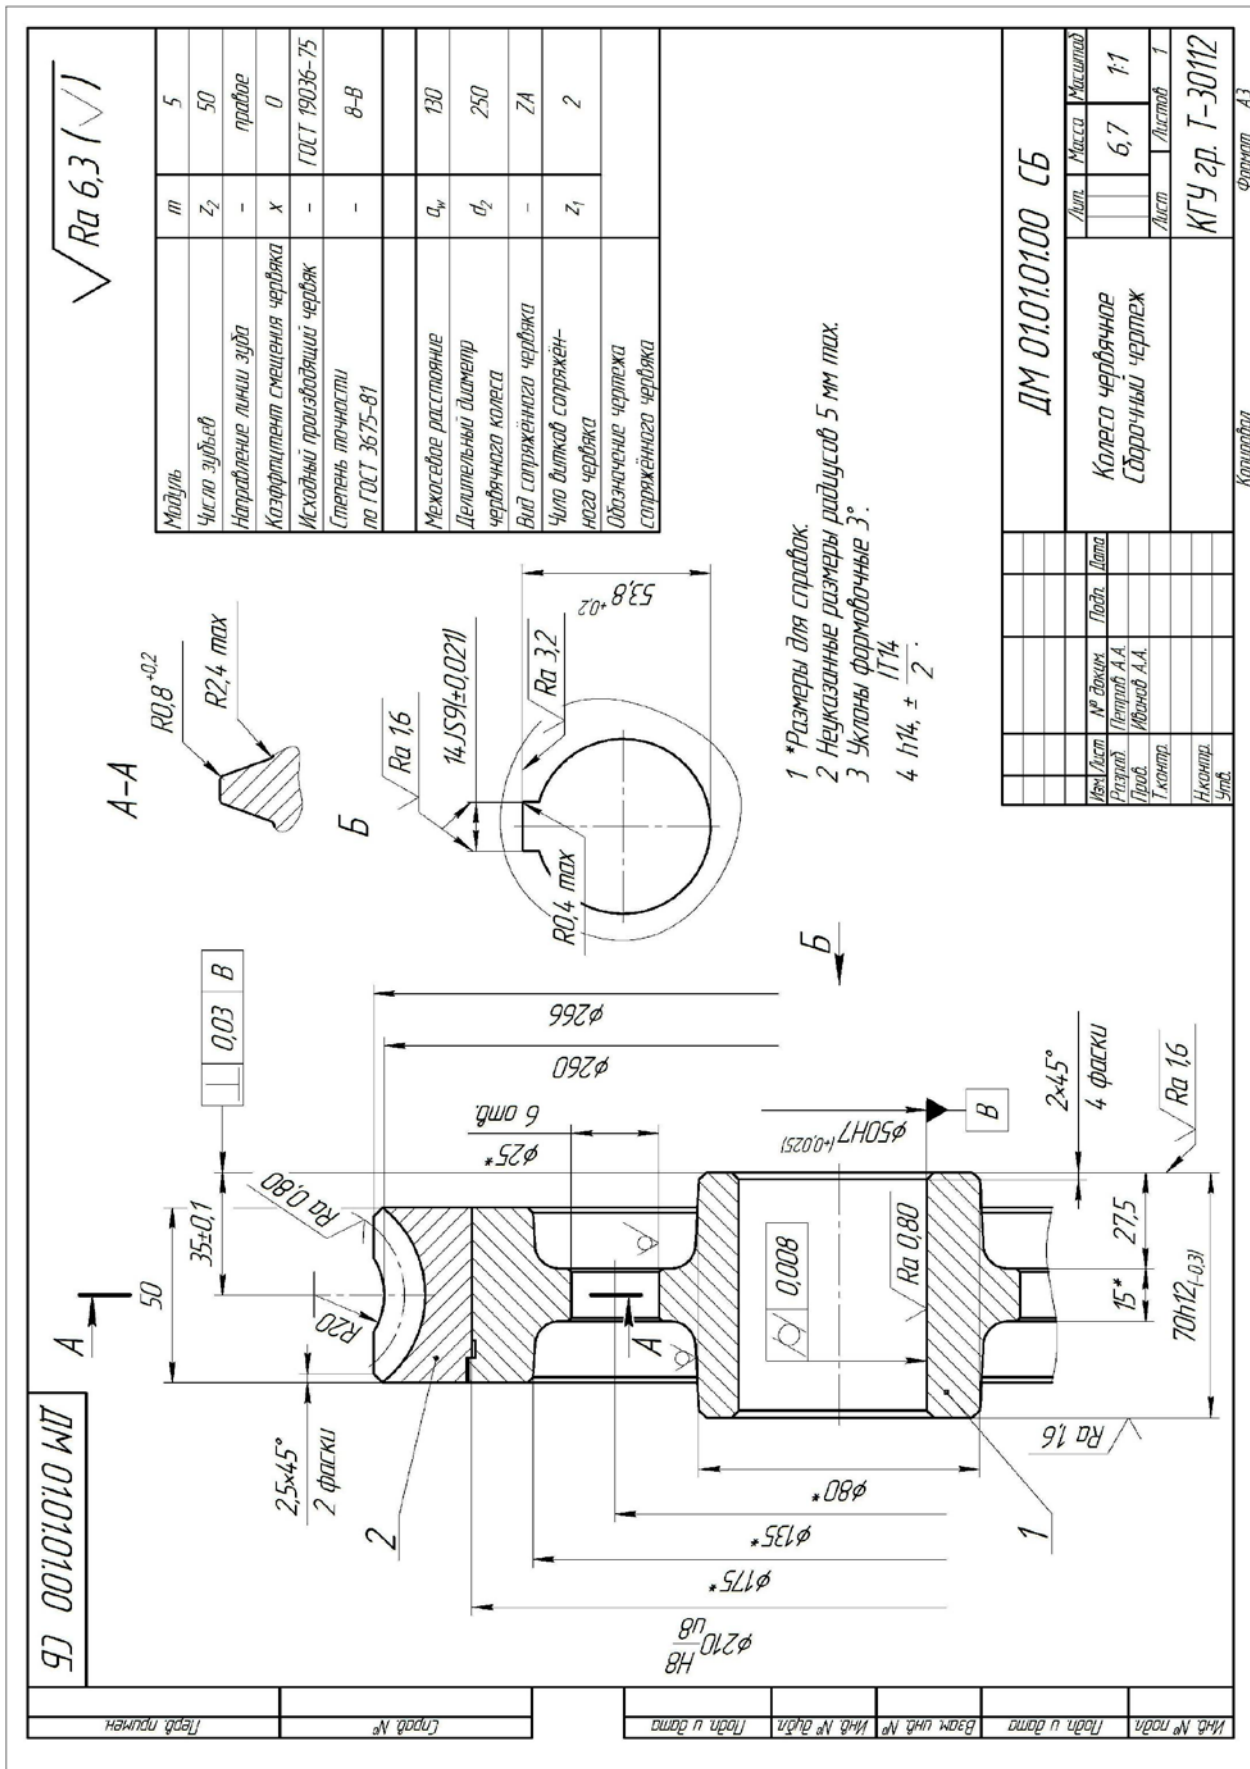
Рабочий чертеж (червячное колесо)
